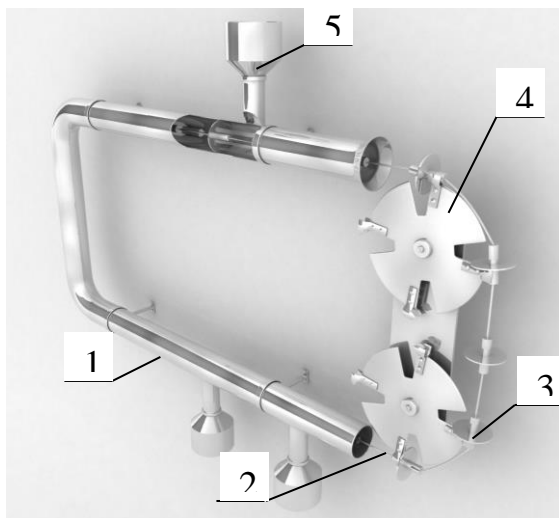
Конструкція гнучкого канатного конвеєра [282]: 1- механізм транспортування вантажу; 2- канат; 3- робочий диск
